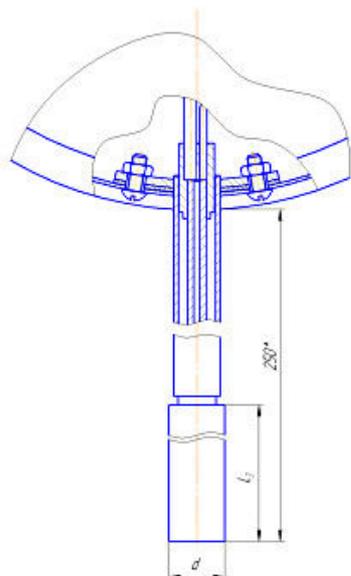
Габаритные, присоединительные и монтажные размеры термометров
